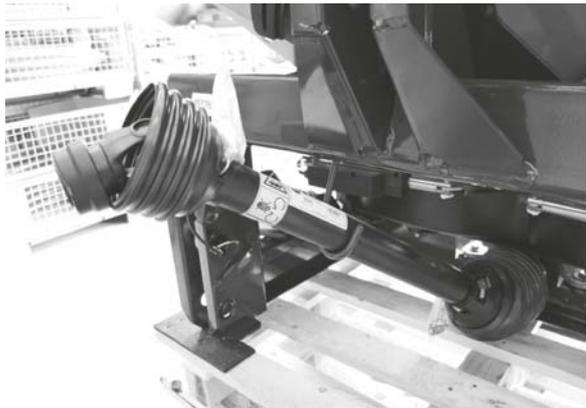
Держатель для карданного вала и гидравлических шлангов
